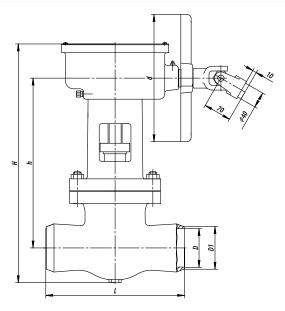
Задвижка DN80-100 с коническим редуктором
